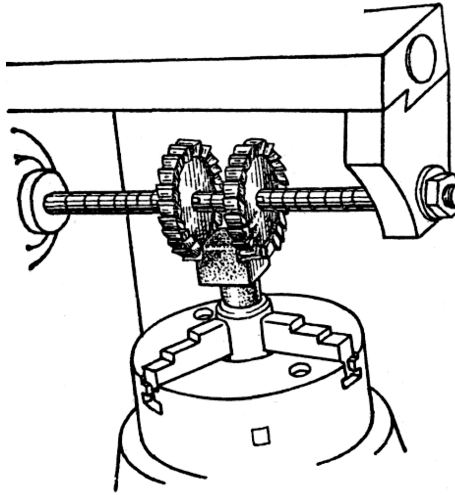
Схема фрезерования граней головки винта набором фрез
